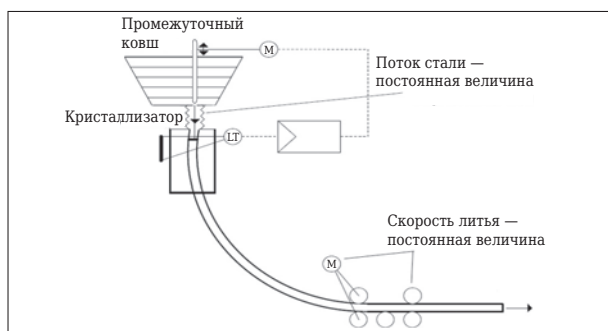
Схема системы регулирования уровня металла в кристаллизаторе для стопорной разливки: М — исполнительный привод тянущих валков или стопорного механизма; ЛТ — датчик уровня металла в кристаллизаторе
